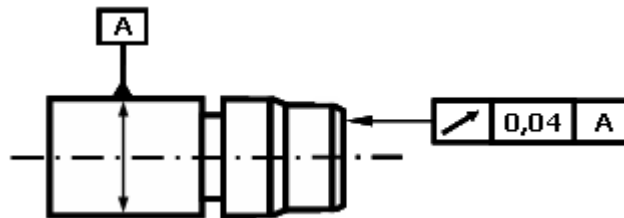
Indicação de tolerância de batida axial em desenho técnico
